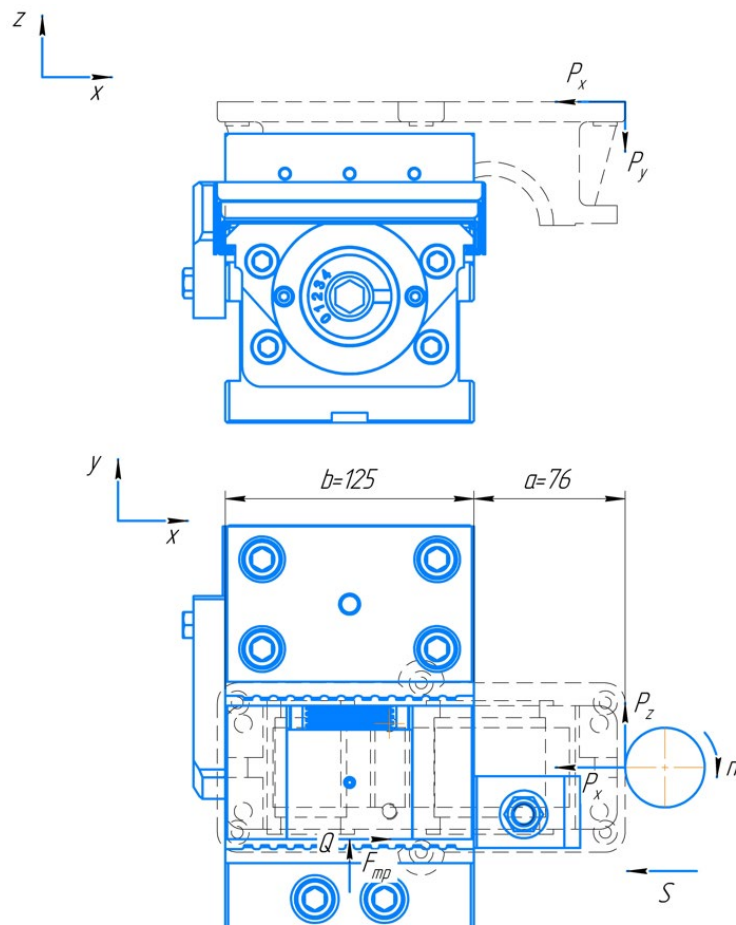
Схема розташування складових сил різання при фрезеруванні.
